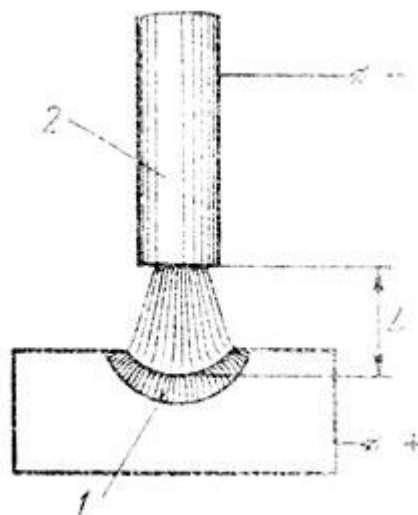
Сварочная дуга: 1 - сварочная ванна, 2 - электрод; L - длина дуги
